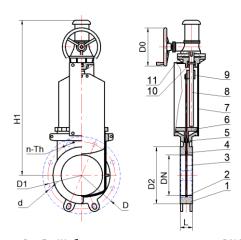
Шиберная задвижка с редуктором DN 50 – 900
